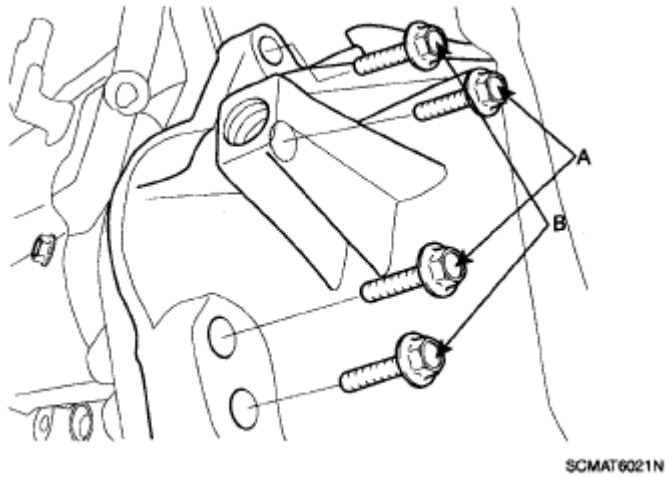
La identificación de los pernos de montaje del motor de arranque y pernos
